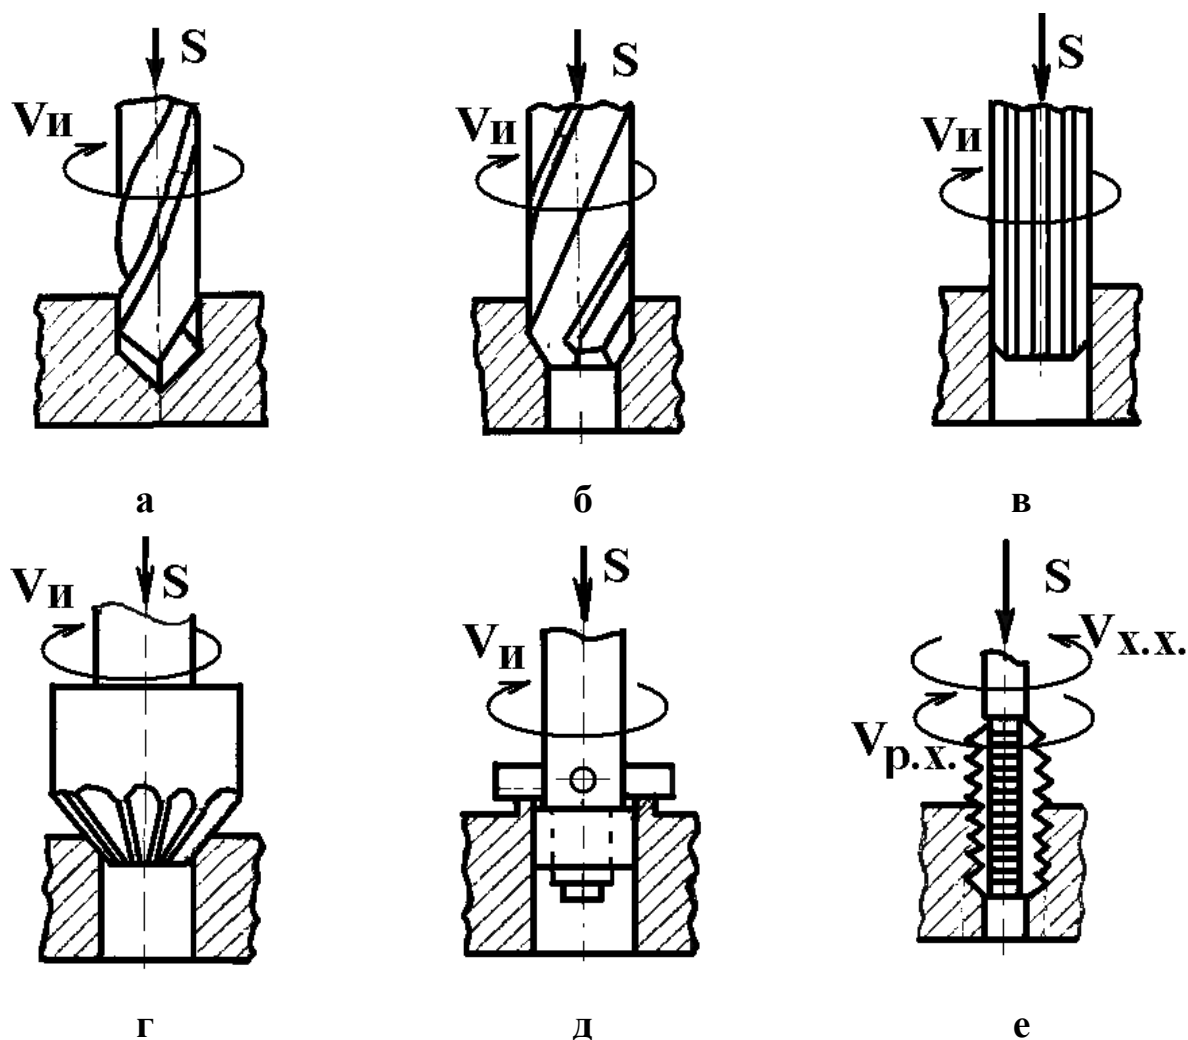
Типовые схемы обработки на сверлильных станках:
